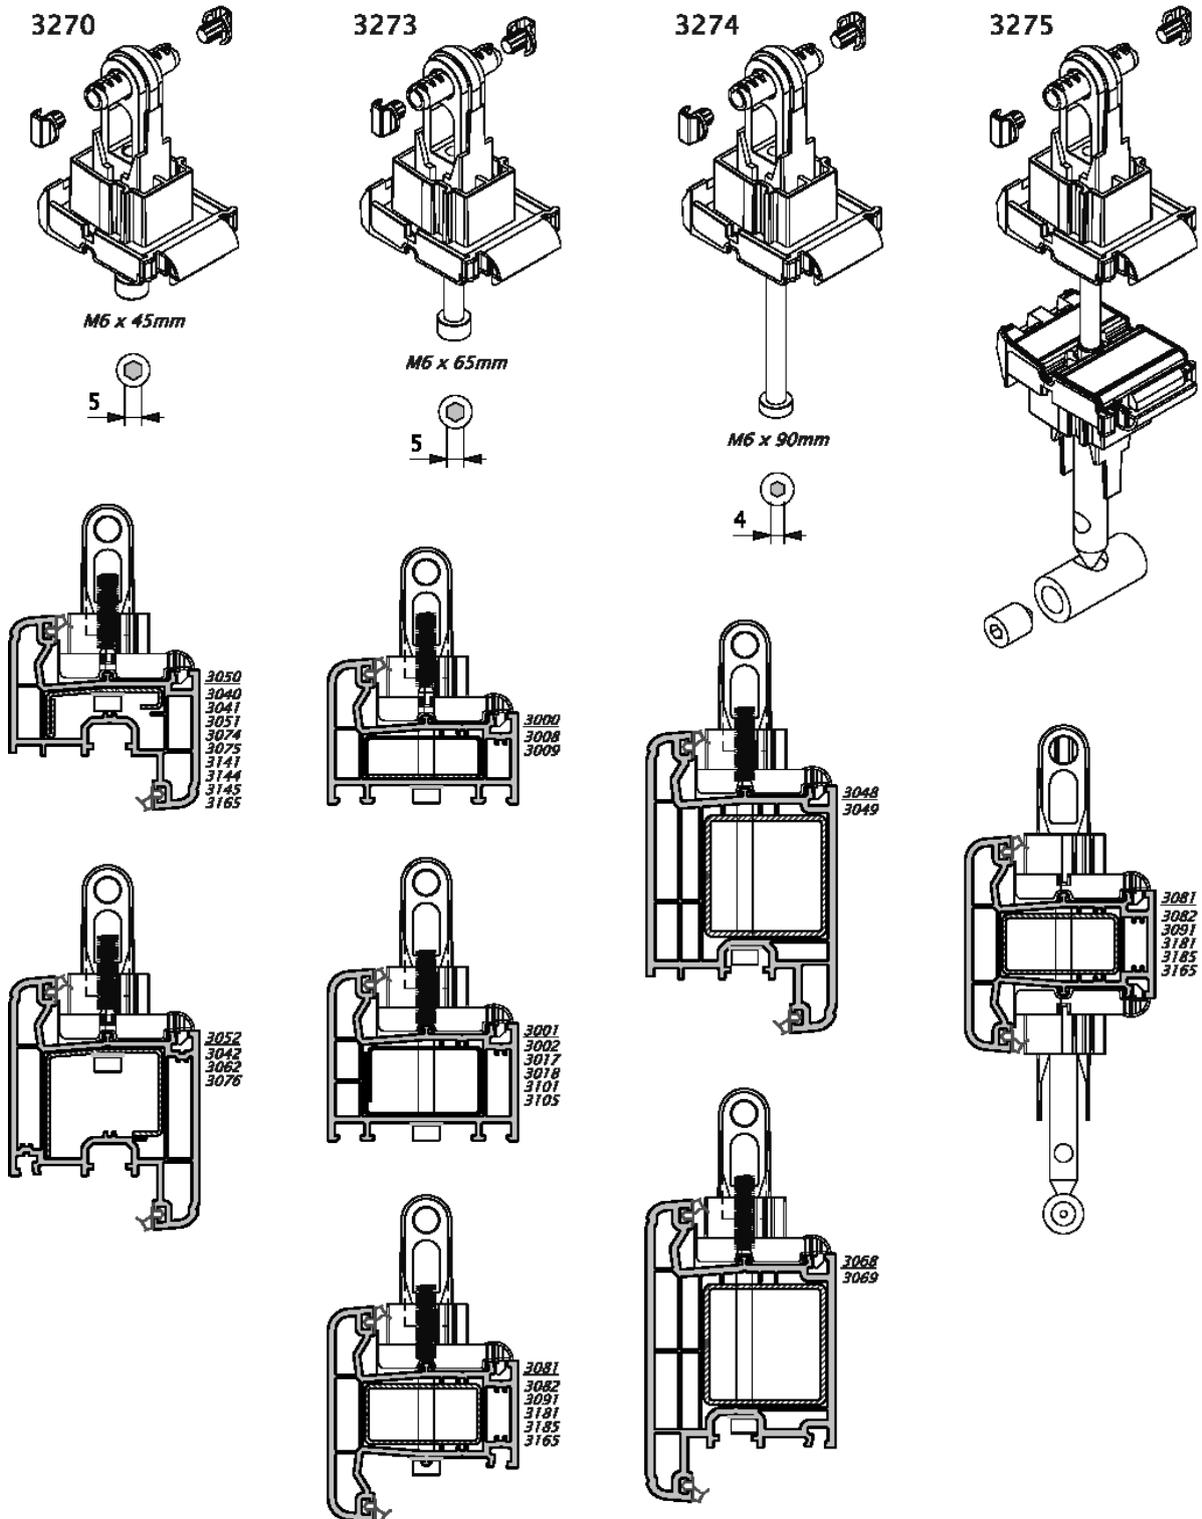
Assemblage mécanique - type boulon ZAMAC
